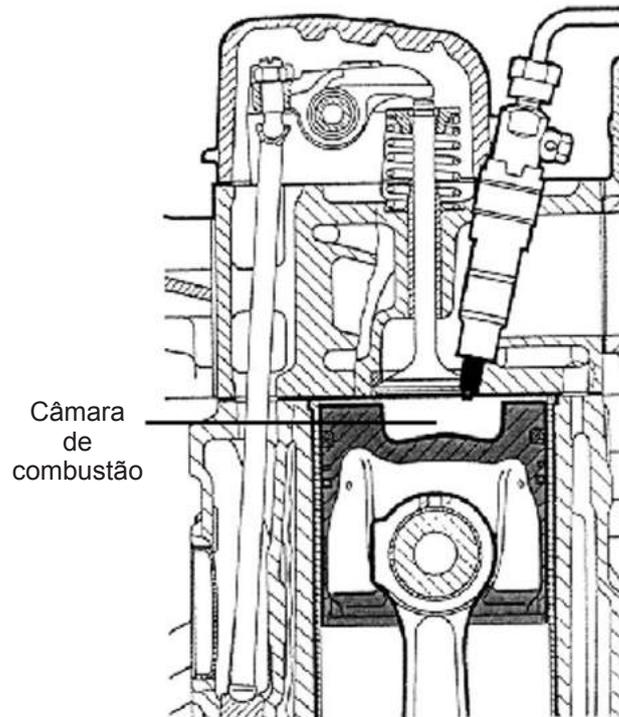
Câmara de combustão (motor Diesel de injeção directa)
